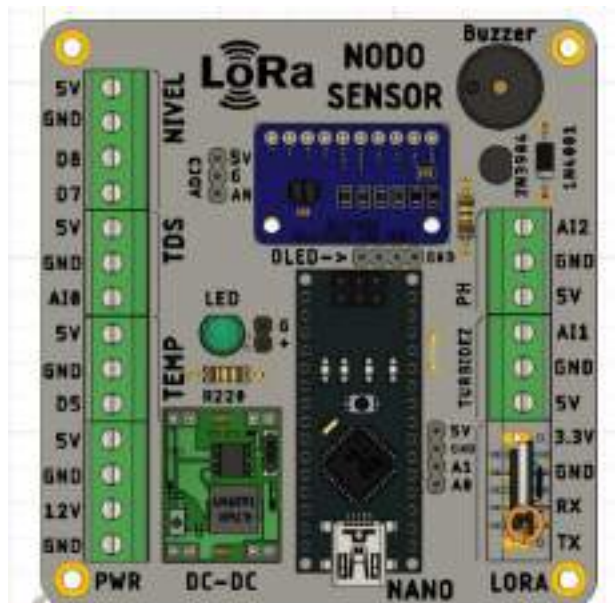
Diseño de placa PCB en 3D del nodo esclavo
